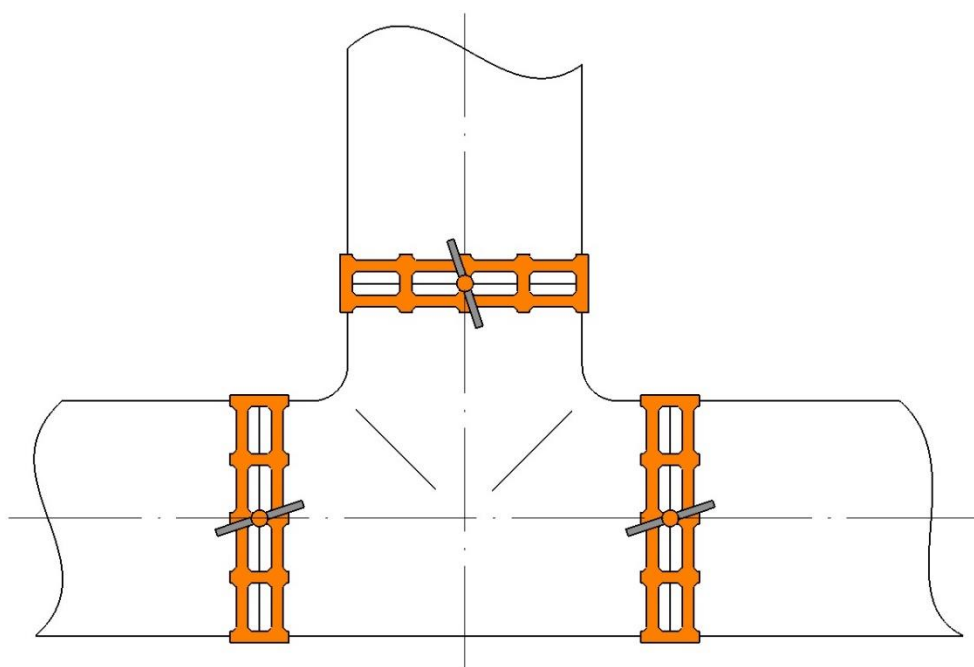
Схема закрепления готового трубопровода к сварке
